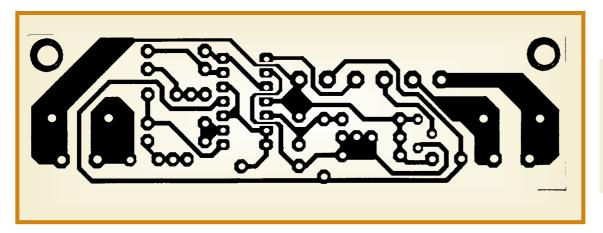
Lado del cobre de la plaqueta de la plaqueta del receptor.
